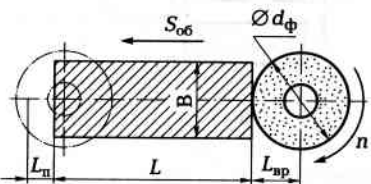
Схема обработки плоской поверхности торцевой фрезой
